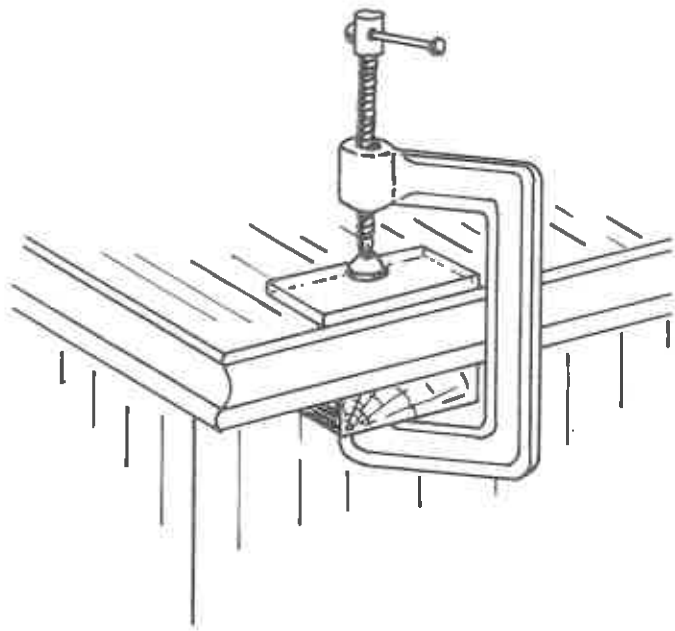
Un morceau de Plexiglas est placé sous les mâchoires du serre-joint avant de presser le nouveau placage.
